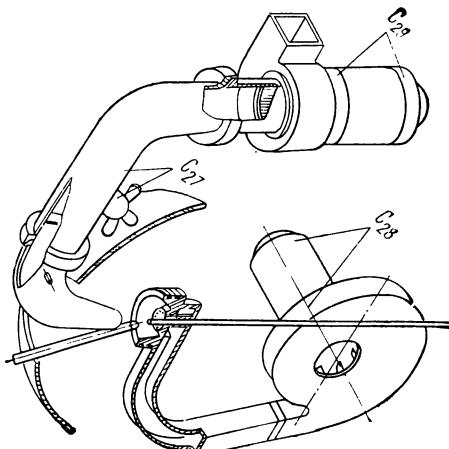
Схема расположения нагнетающего, отсасывающего и осевого вентиляторов с указанием точек смазки шарикоподшипников электродвигателей
